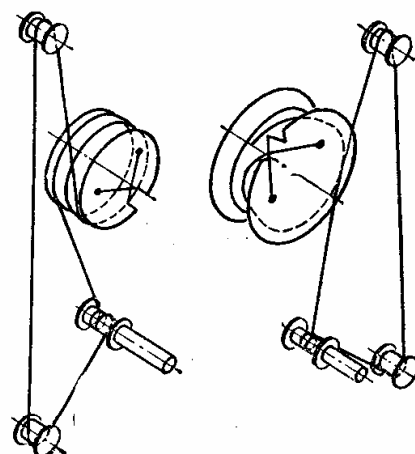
Кинематическая схема верньерного устройства радиоприемника «Ленинград-002»
